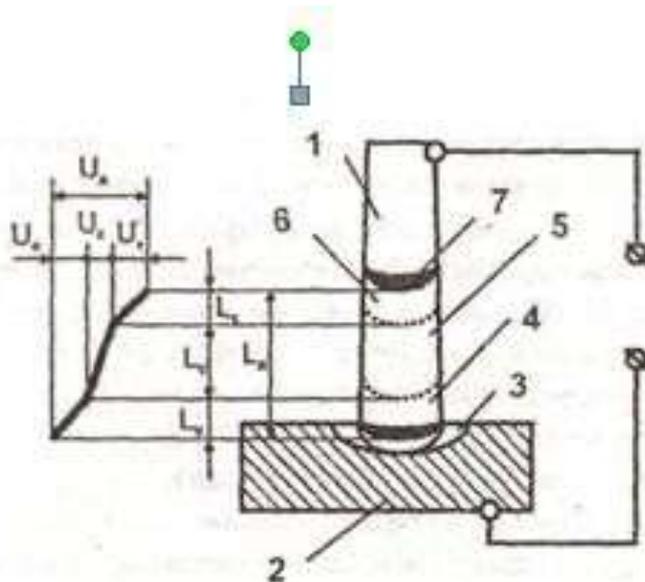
Схема сварочной дуги и падения напряжений в ней:
